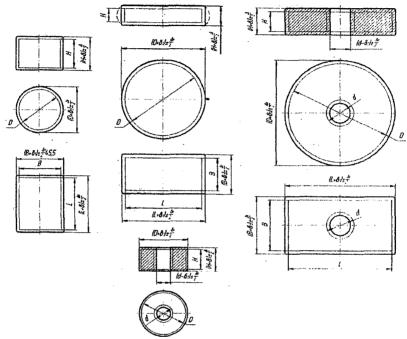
Схема назначения припусков и допусков для поковок 2-ой группы
